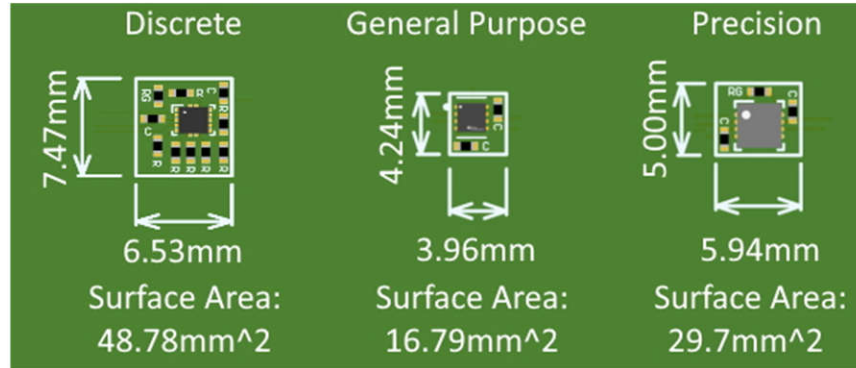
듀얼 공급 IA 회로를 위한 간소화된 PCB 레이아웃 비교.
